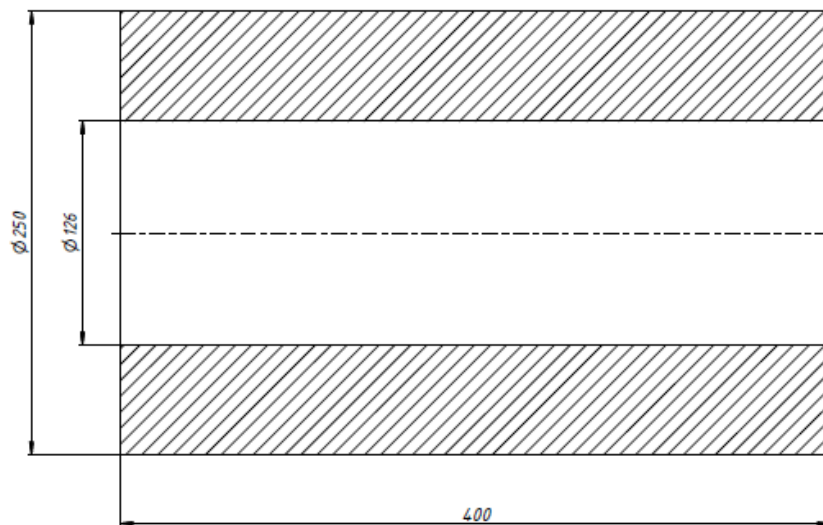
Ескіз заготовки для подальшого оброблення
